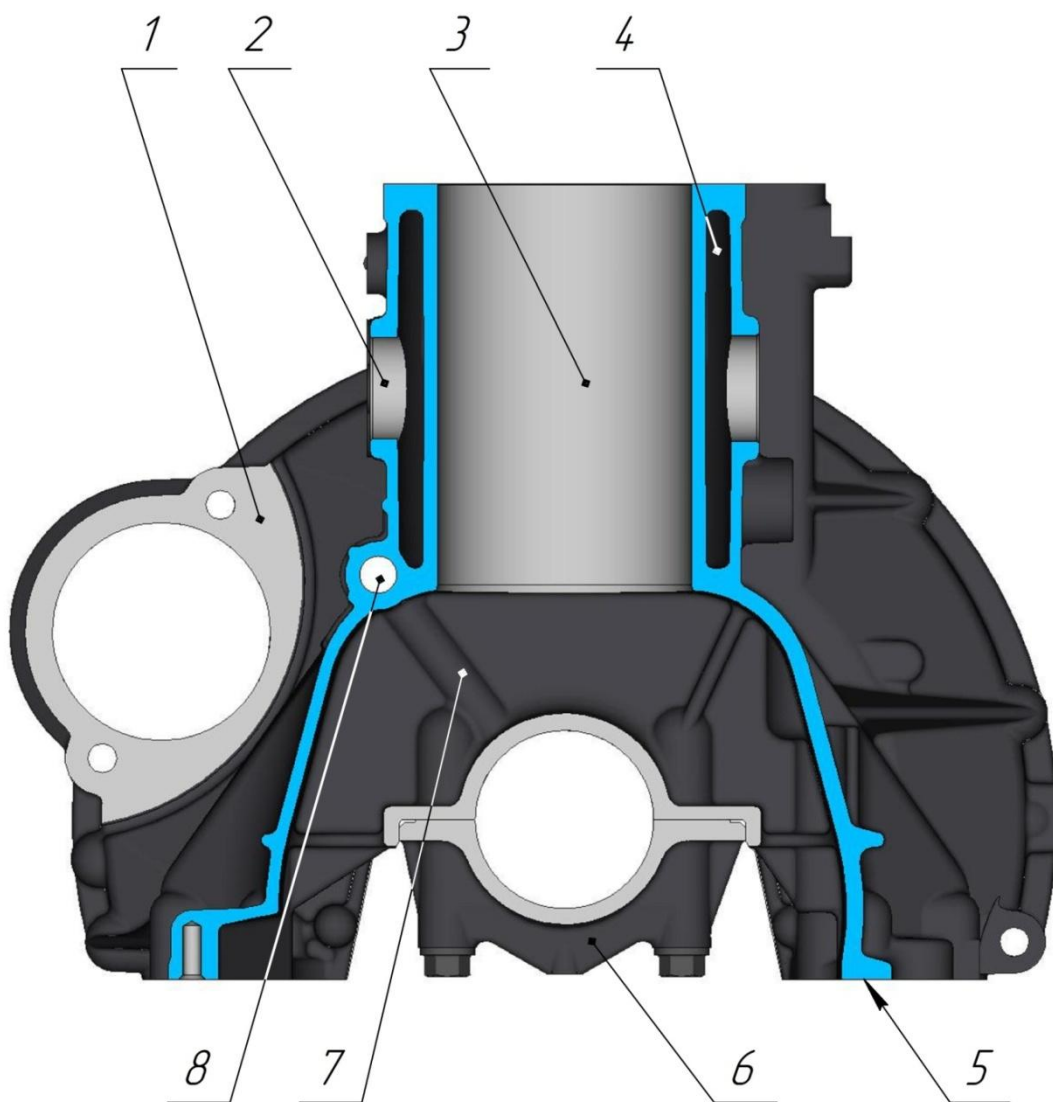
Блок цилиндров. Поперечный разрез по оси цилиндра:
